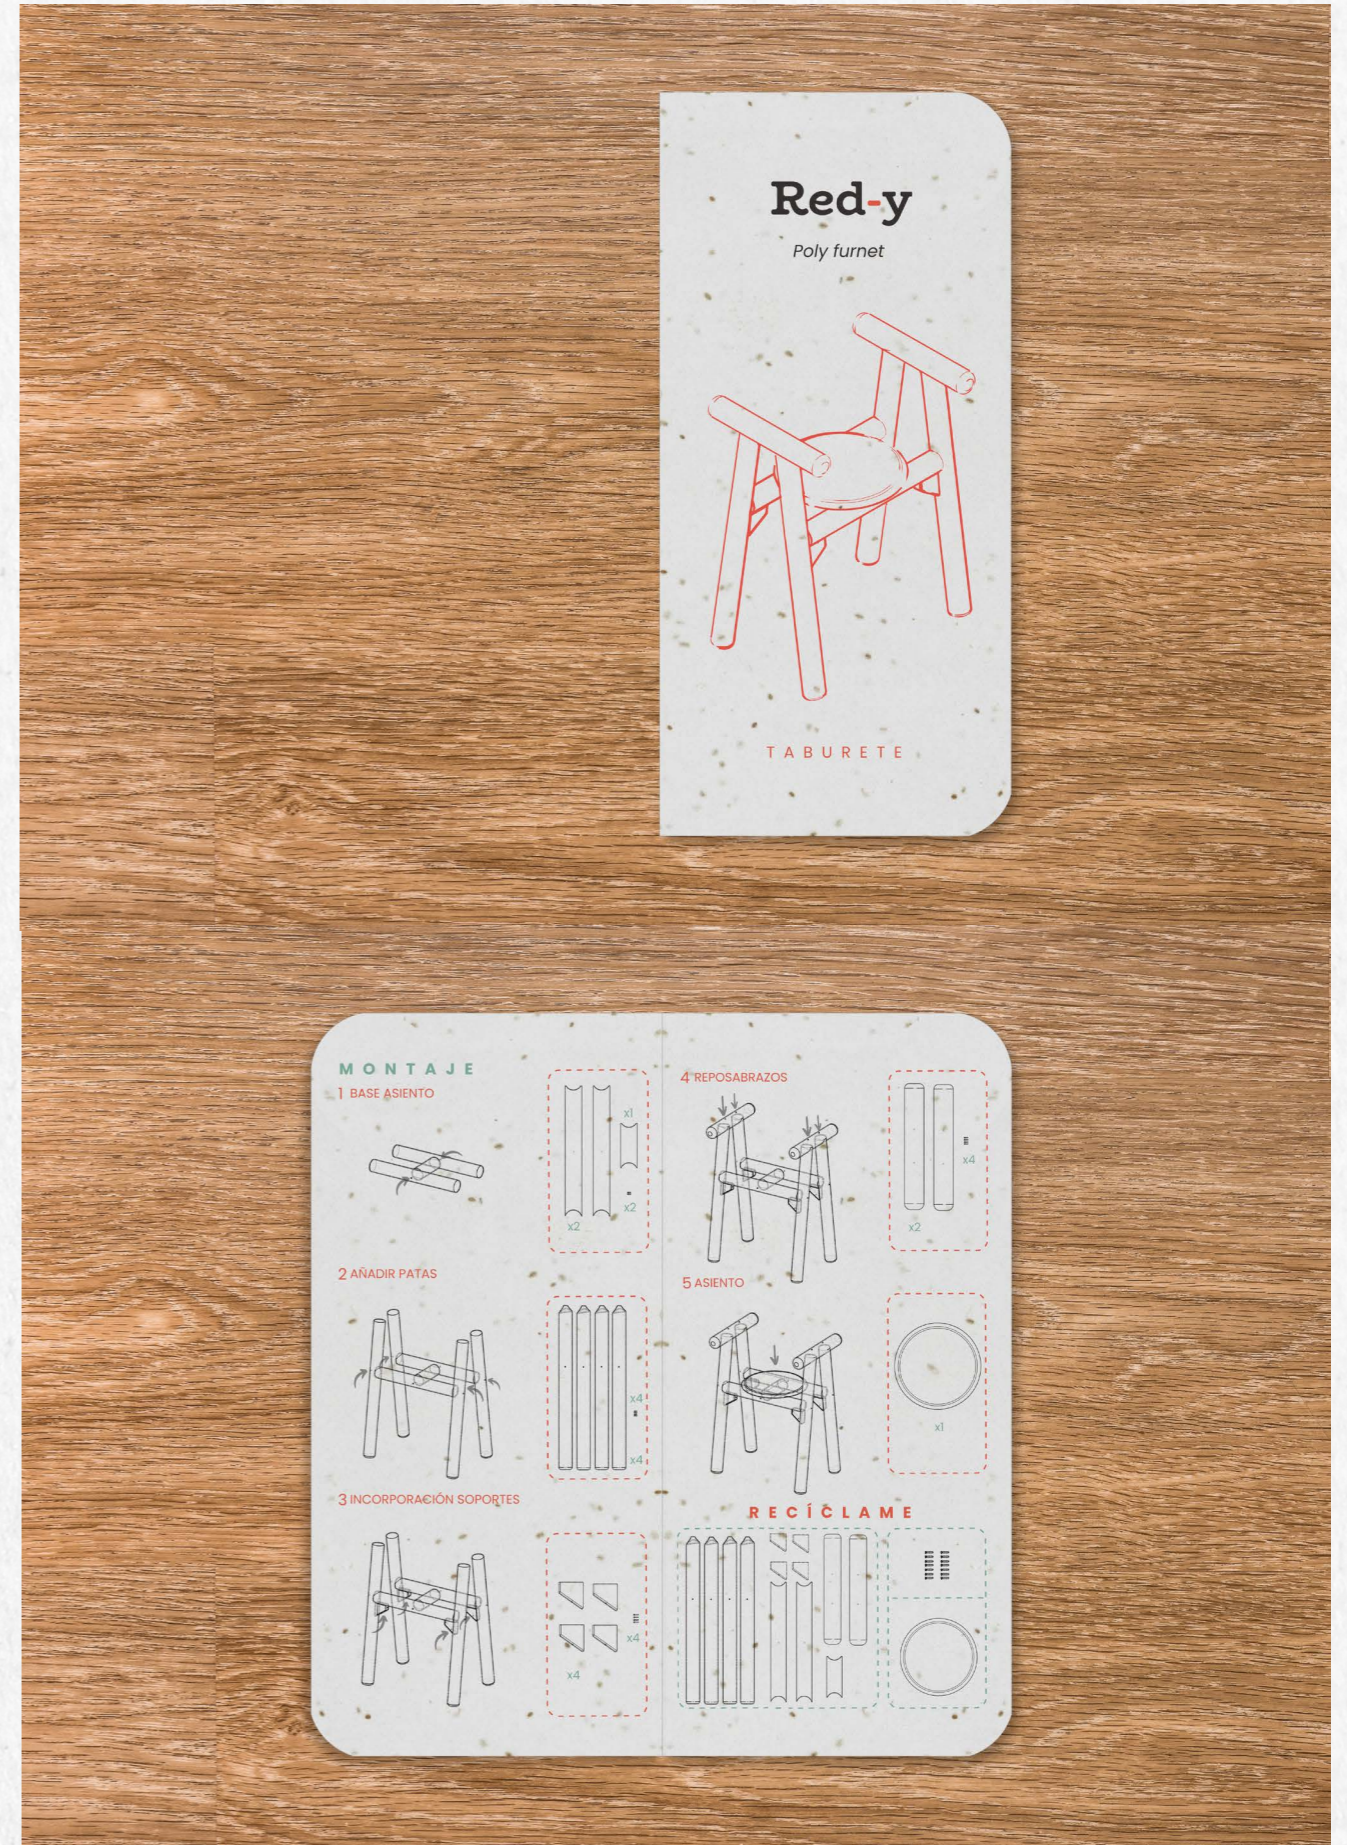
Portada instrucciones plantables de montaje. Creación propia 2024.
